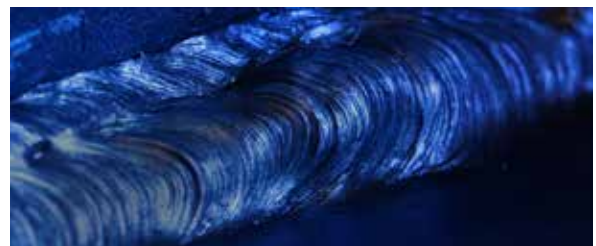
Detailansicht einer unter Wasser geschweißten Kehlnaht
